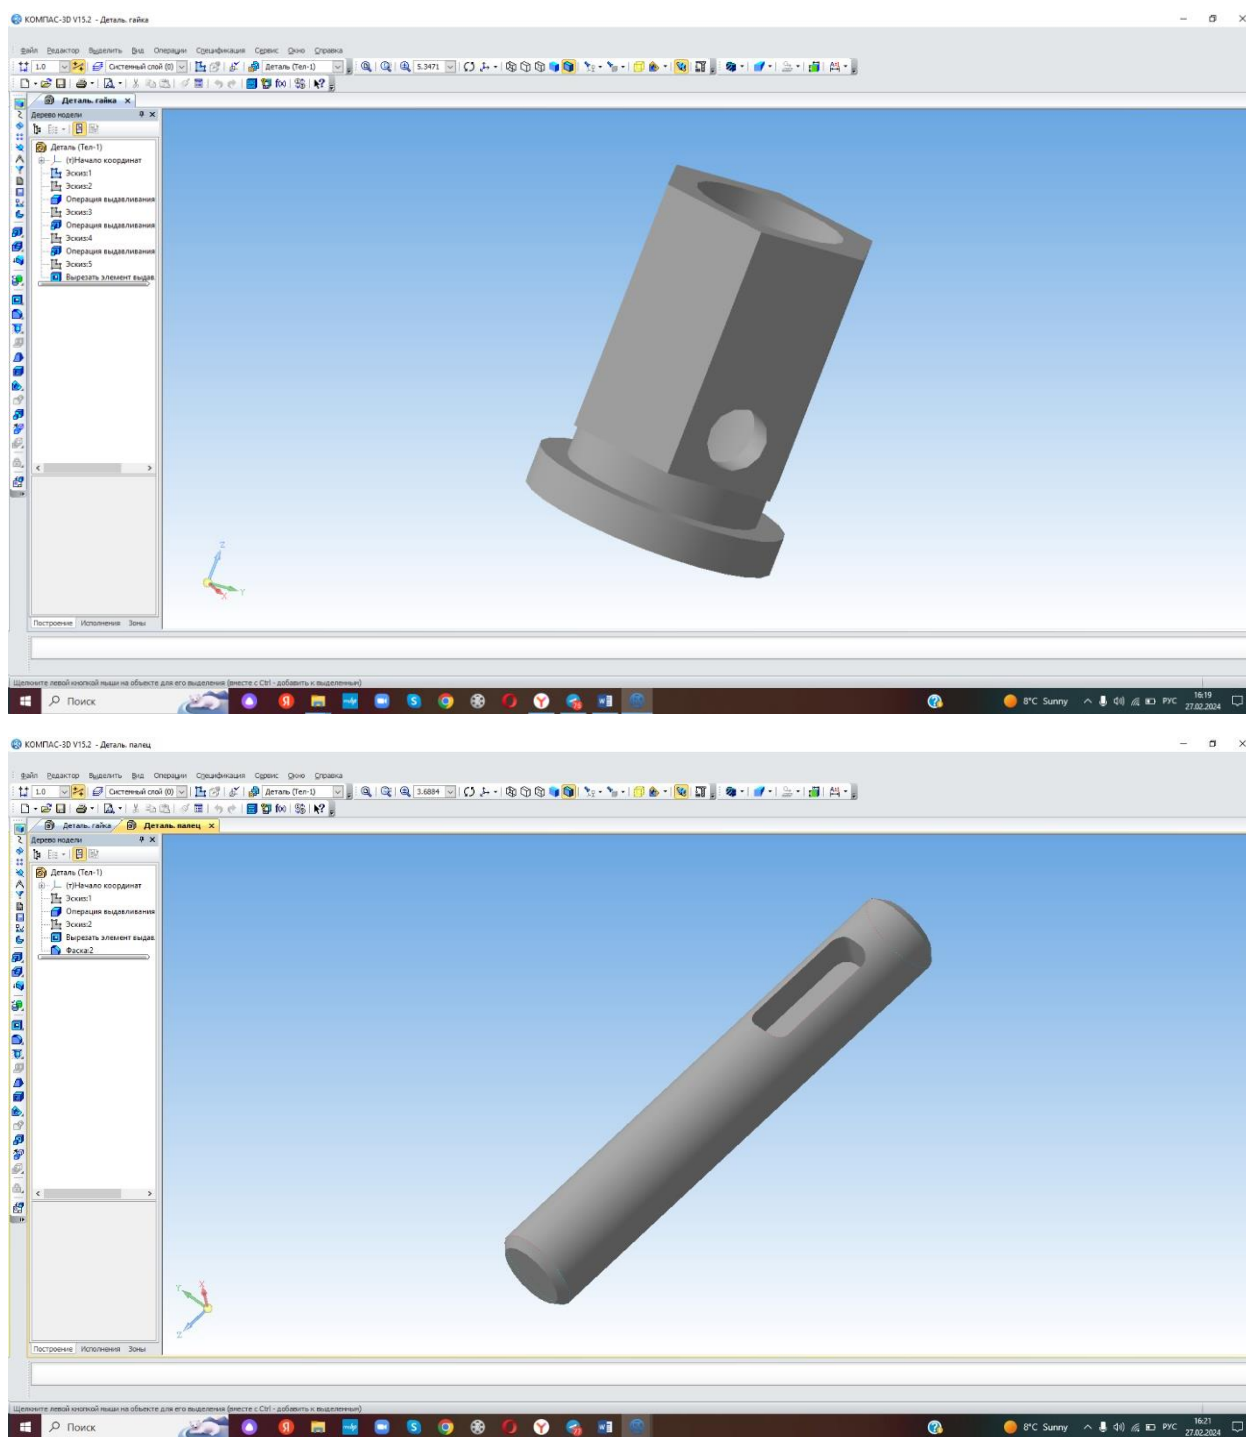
Детализовка сборки дросселя – корпус и ось
